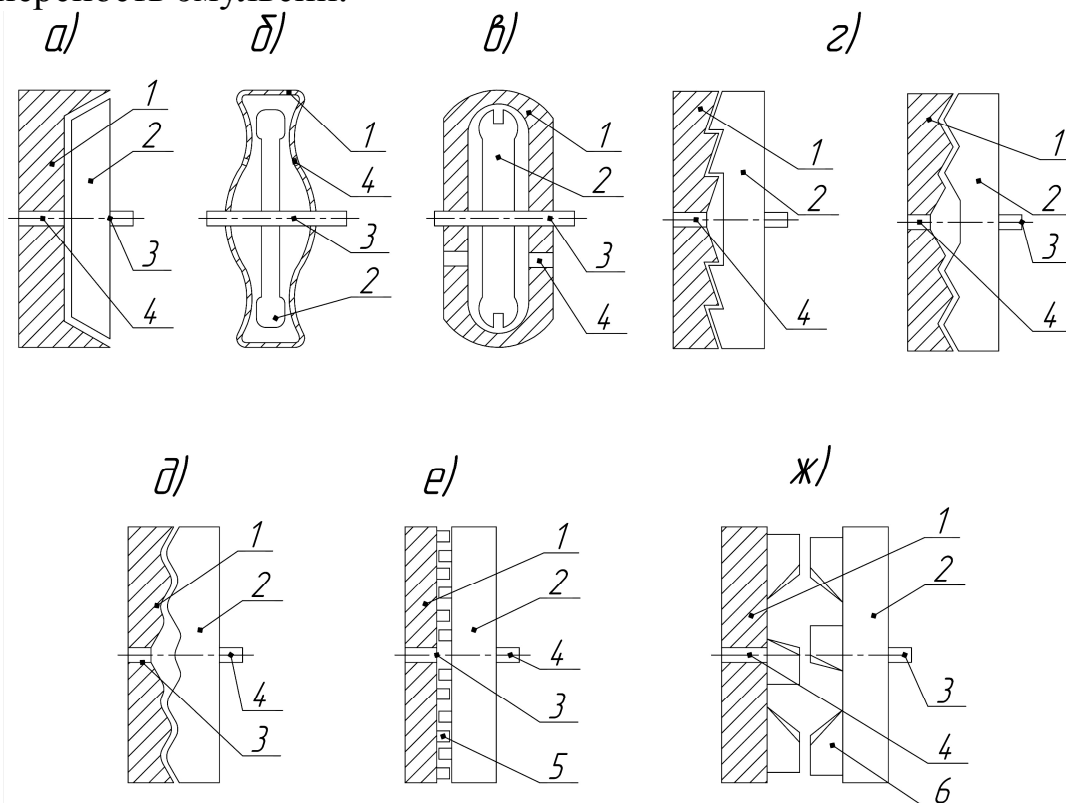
Виды рабочих поверхностей диспергаторов роторного типа:
